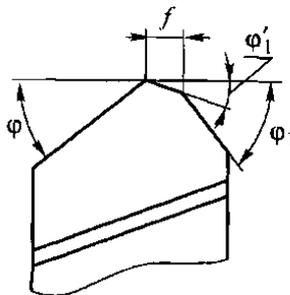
Заточка вершини токарного резца для вібраційного точення
